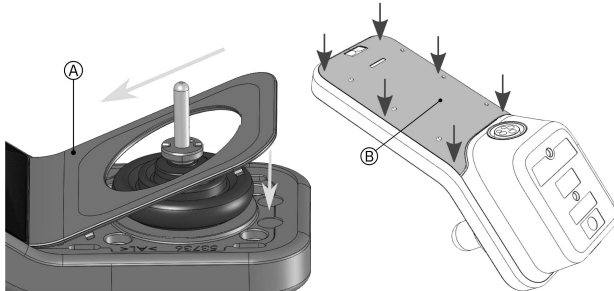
Remplacez le cache décoratif du joystick et le cache arrière
